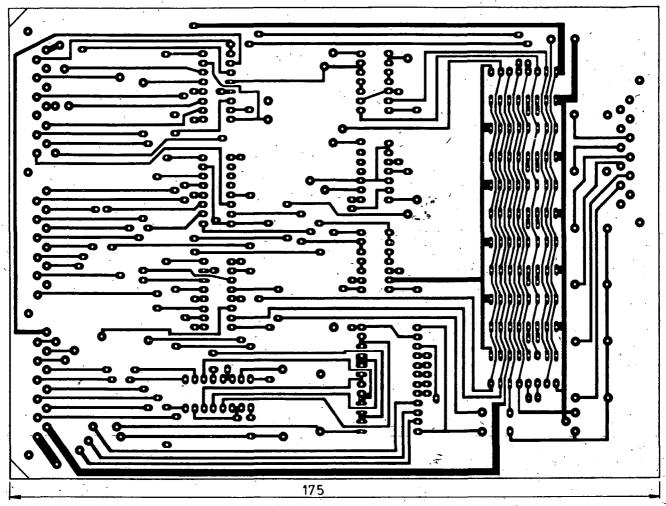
Zapojení desky pamětí a zobrazení T102 \
